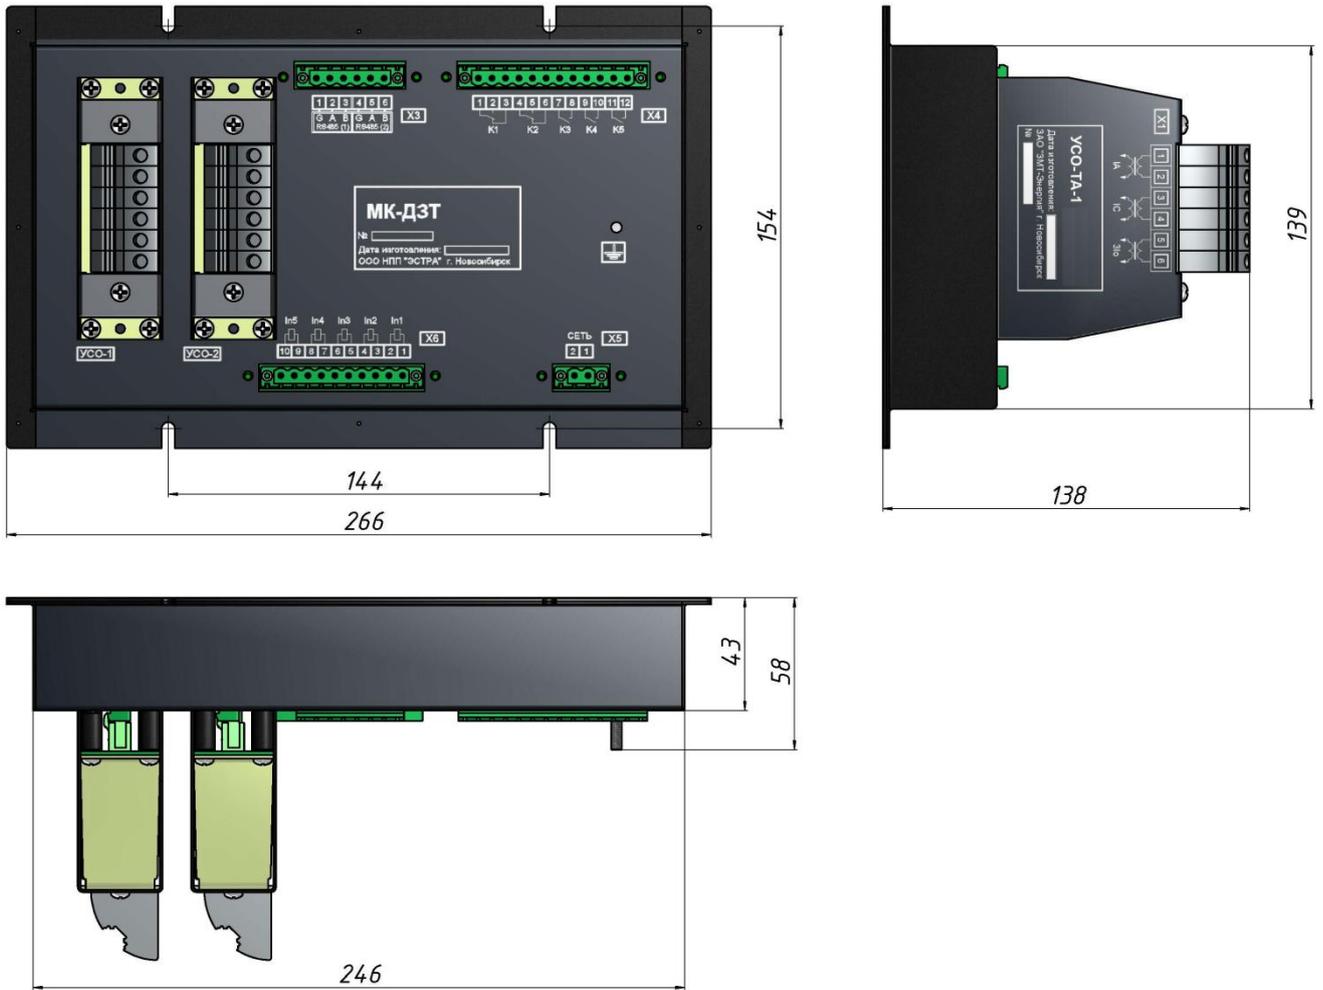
Внешний вид и габаритный чертеж блока с УСО-ТА
